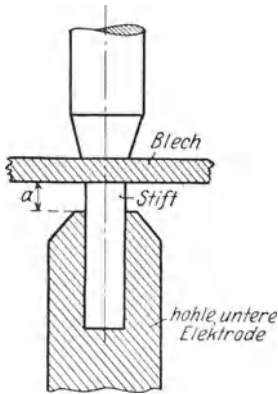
Elektroden für Zapfenschweißung.
